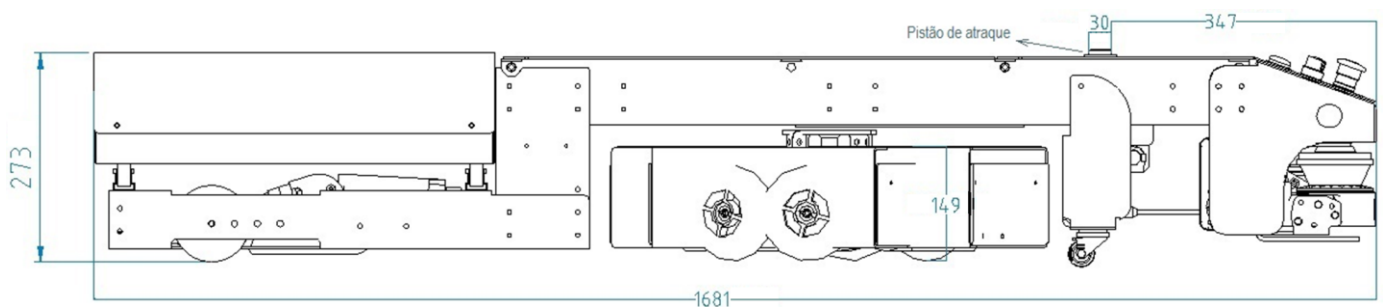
Dimensões [mm] críticas do AGV ASTI - EasyBot
